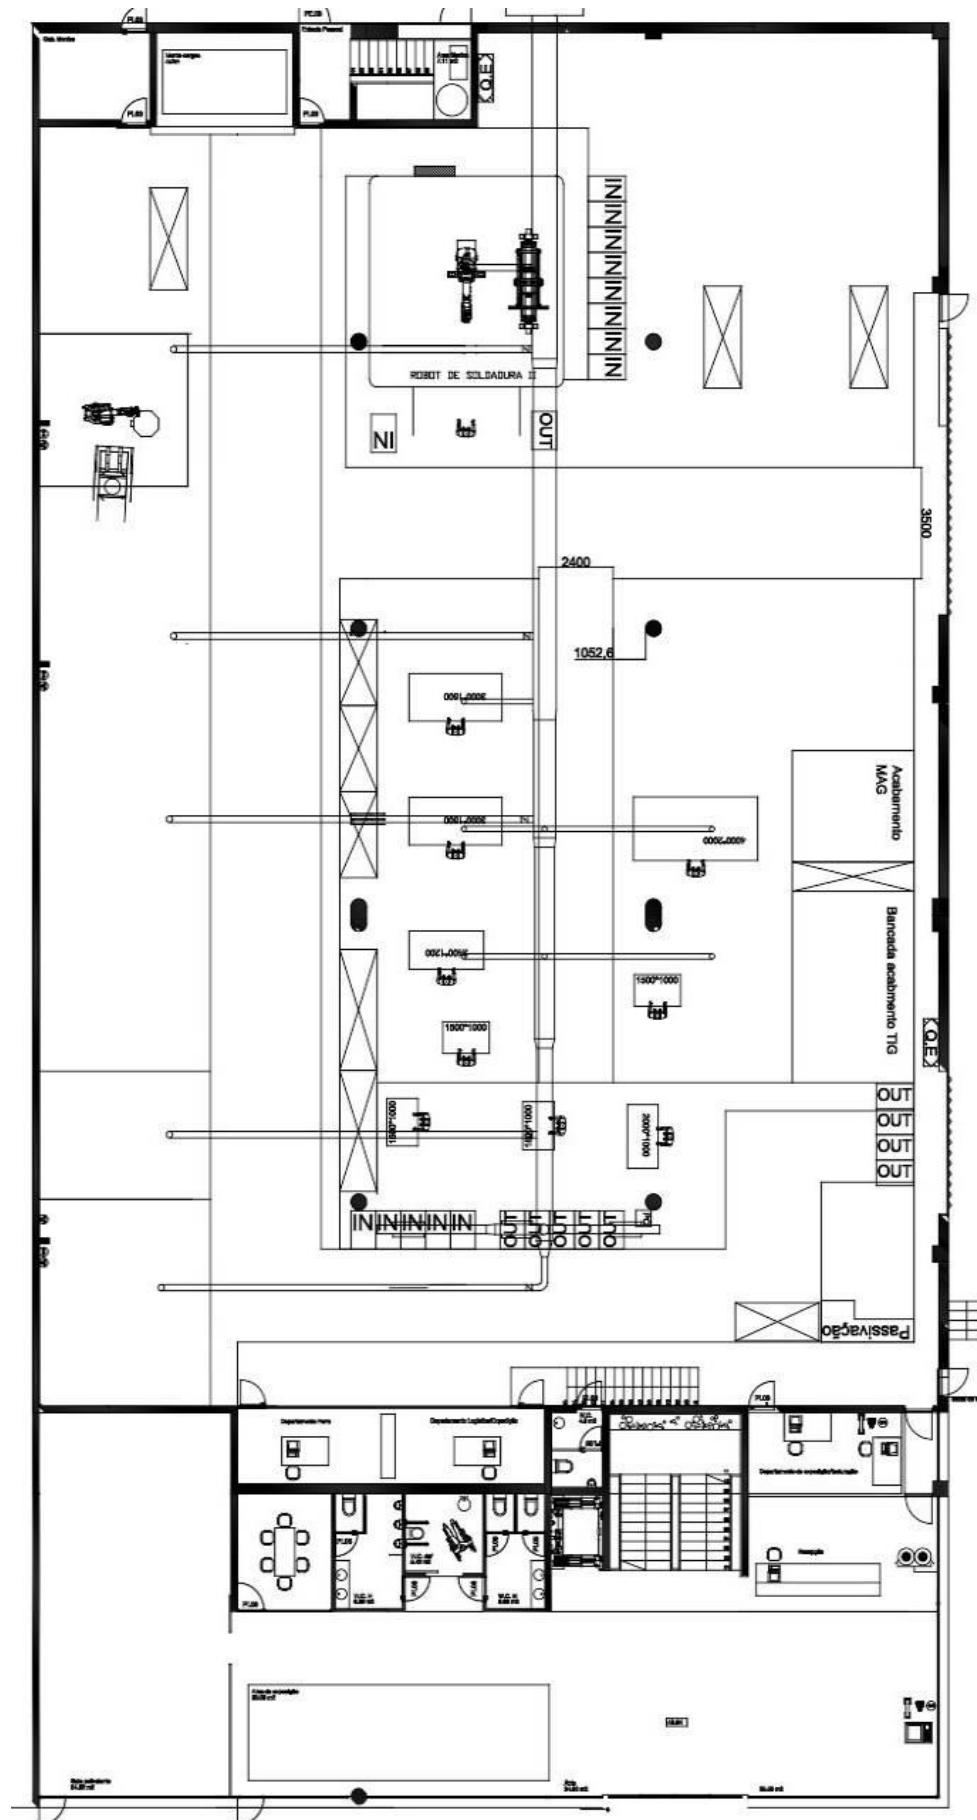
Planta do Pavilhão Cave do Chão de Fábrica
